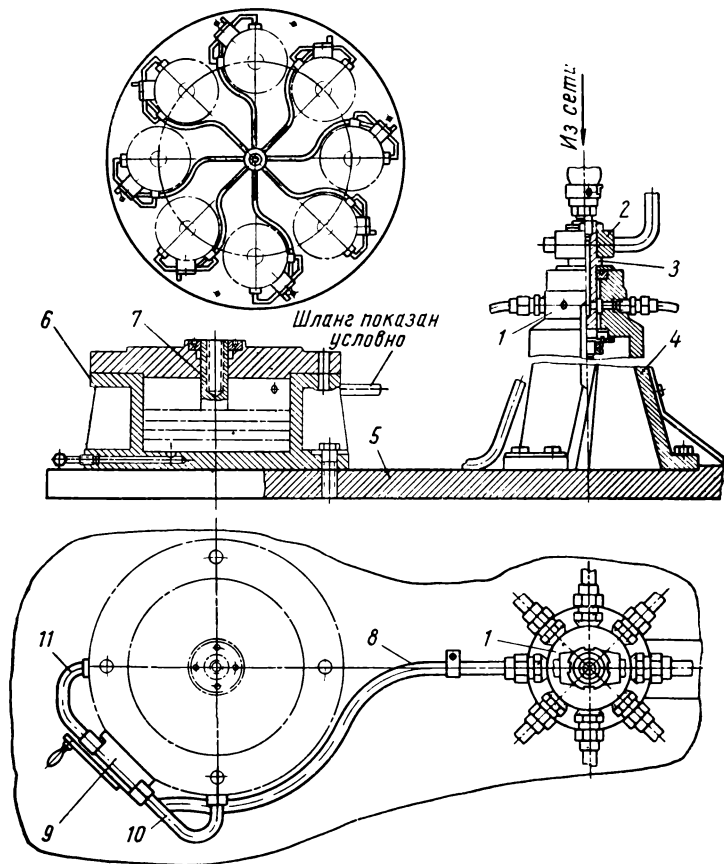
Схема привода восьми приспособлений, установленных на вращающемся столе
